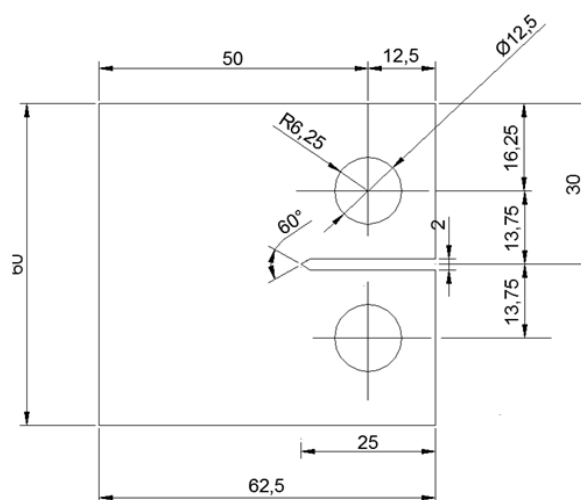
Dimensions de l'éprouvettes CT50 utilisé pour les essais de fissuration.
